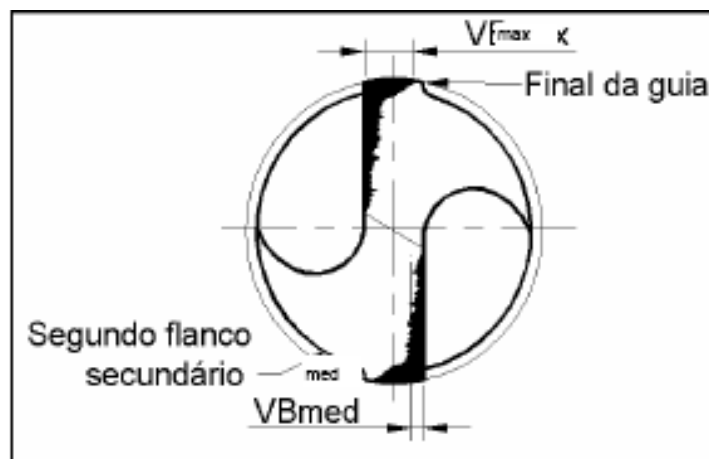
Medição de desgastes de flanco (Bork, 1995).
